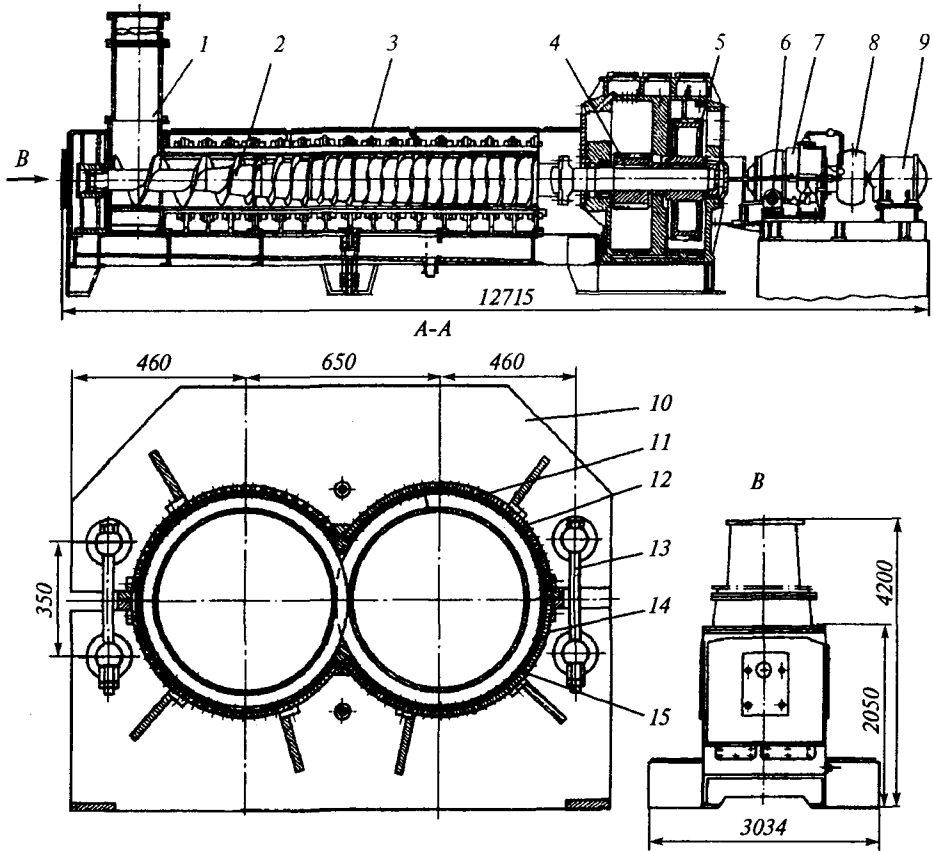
Горизонтальный двухшнековый пресс «Stord BS-64»
